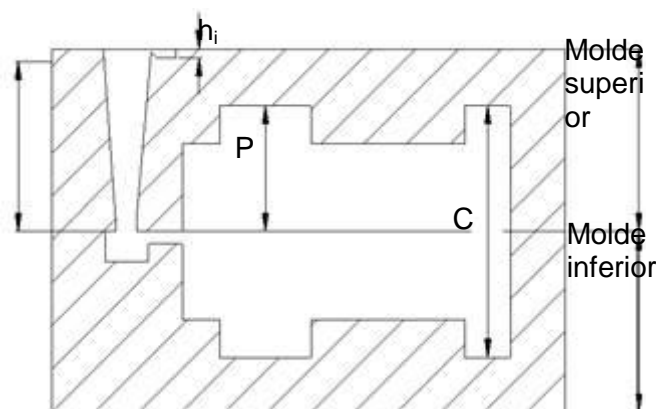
Corte transversal para el diseño de los componentes del molde.
